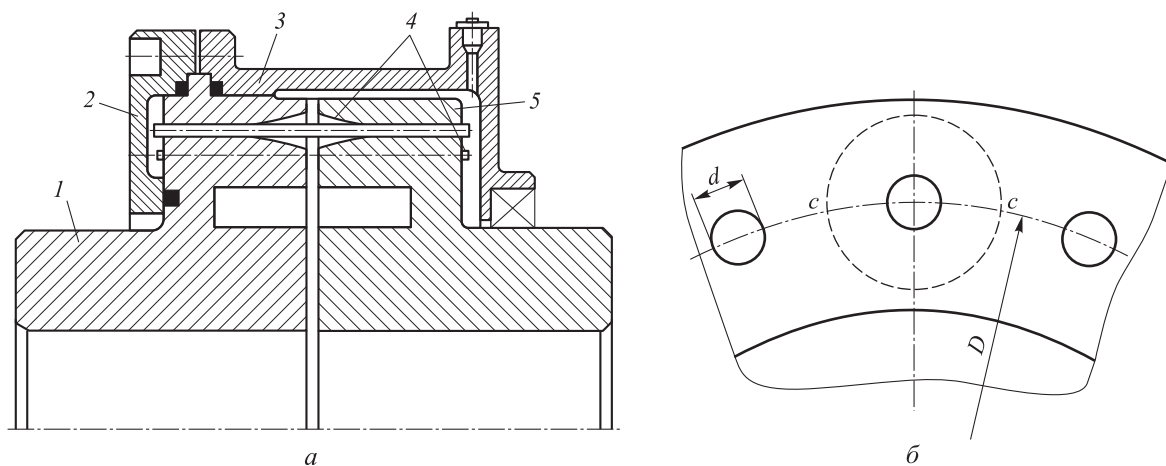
Схемы муфты со стальными упругими стержнями круглого сечения: а — ее продольный разрез; б — однорядное расположение стержней
